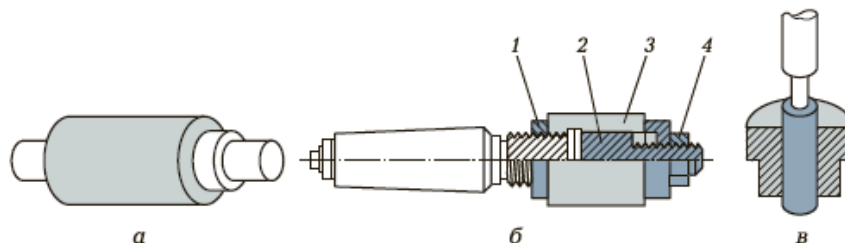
Цилиндрические притиры: а — нерегулируемый; б — регулируемый: 1, 4 — гайки; 2 — коническая оправка; 3 — разрезная втулка; в — пример использования
